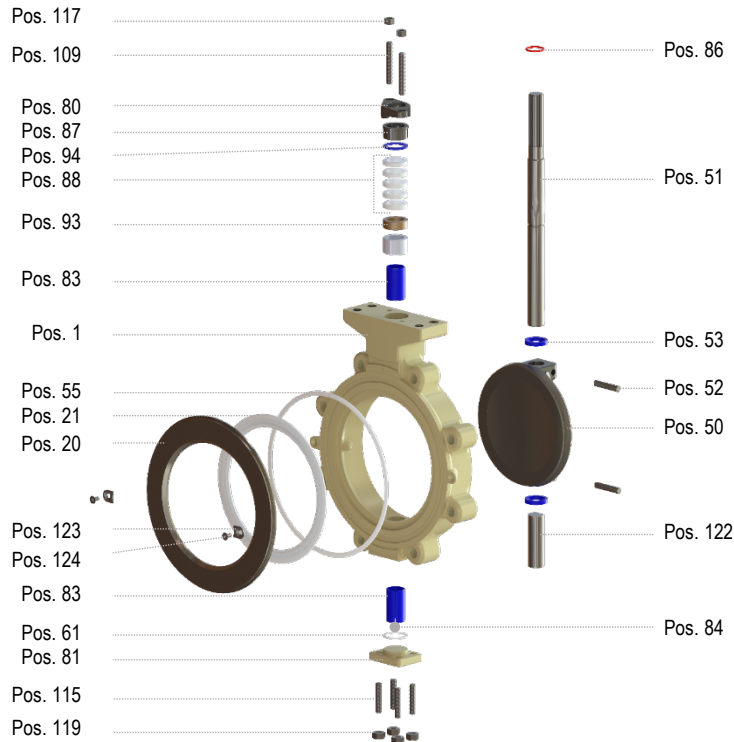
Explosionszeichnung eines Ventils in Anflanschführung.
